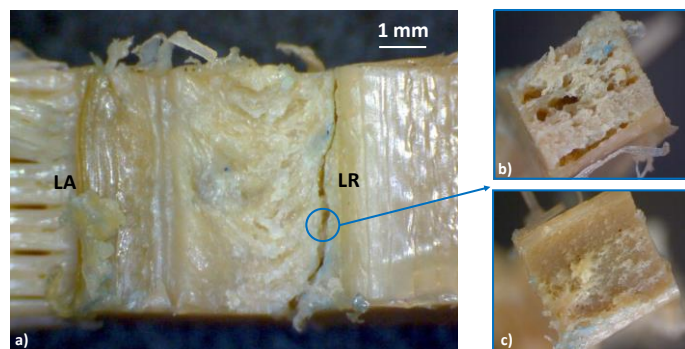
Macrografia do provete após Ensaio 1: a) Superfície superior do provete, b) Superfície de fratura do cordão de soldadura do LR, c) Superfície de fratura da interface do material base com o LR.
